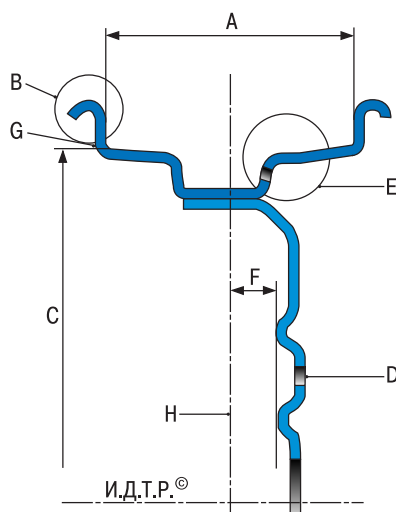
Параметры колесных дисков: A — ширина профиля обода (в дюймах); B — форма бортовой закраины обода; C — диаметр обода (в дюймах); D — количество отверстий под болты крепления колеса; E — профиль борта покрышки; F — вылет ET (в мм); G — точка, в которой измеряется максимальное биение диска; H — центр диска
